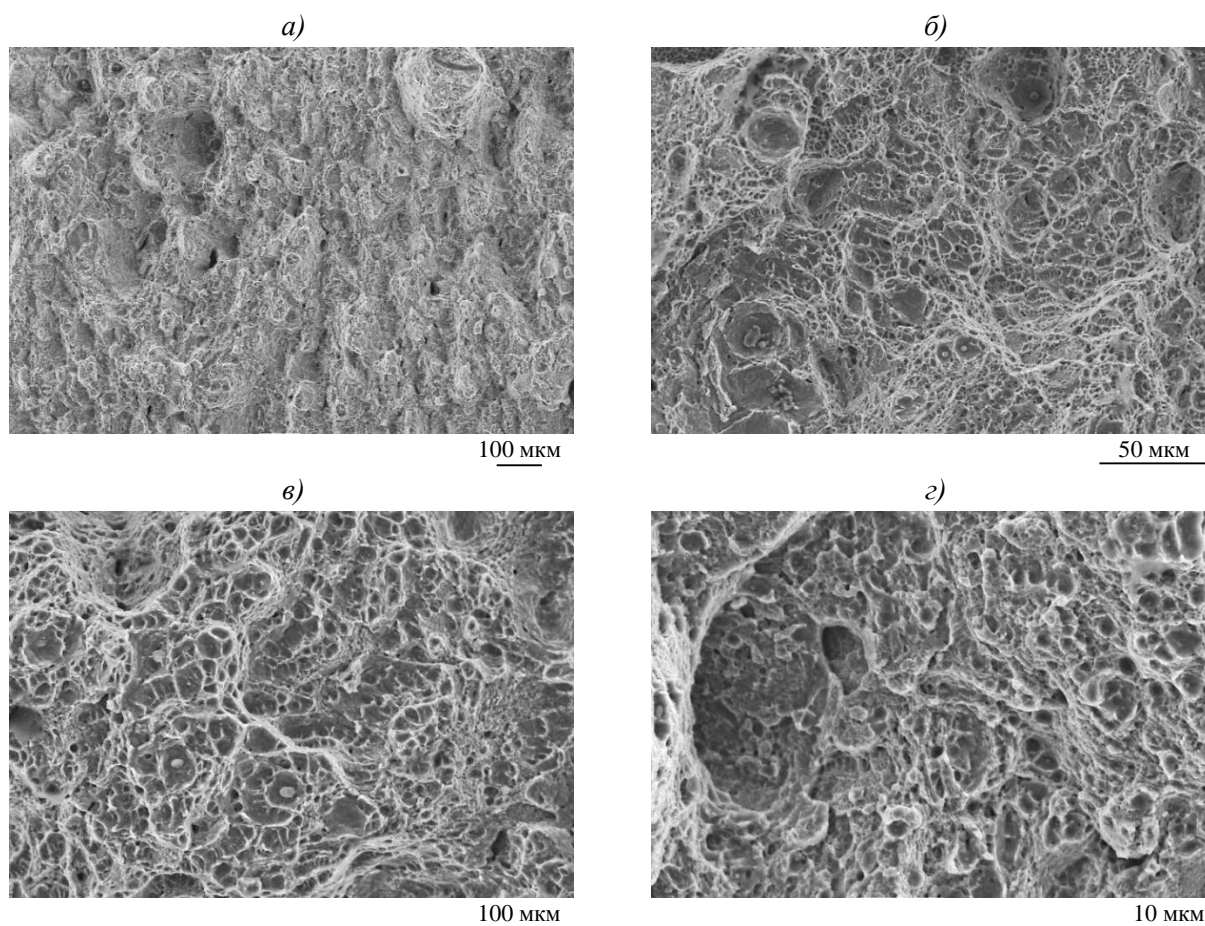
Характерное строение излома ($a - \times 100$; $b - \times 500$; $в - \times 1000$; $г - \times 2000$) заготовки из стали 38ХНЗМФА
